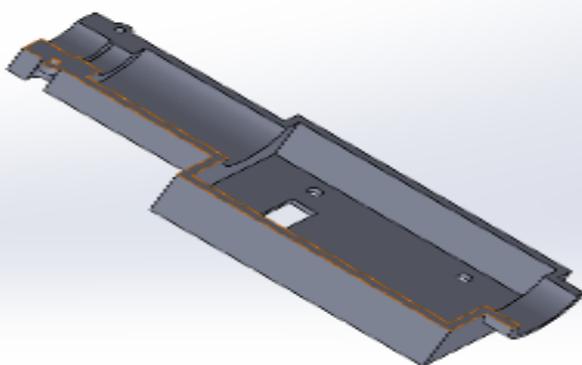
Tutup *casing* motor *stepper*/penggerak *valve* regulator
